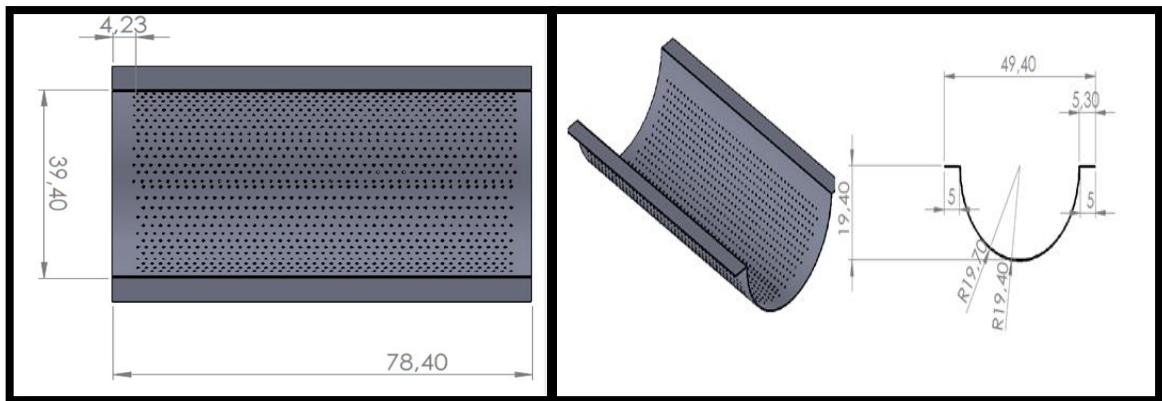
Dimensionamiento de la malla
